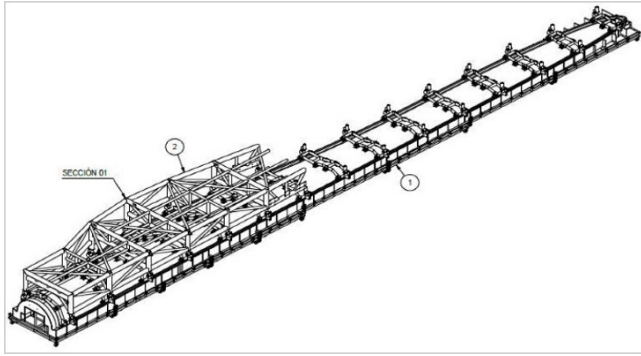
Estructuras metálicas de 1er y 2do nivel.
